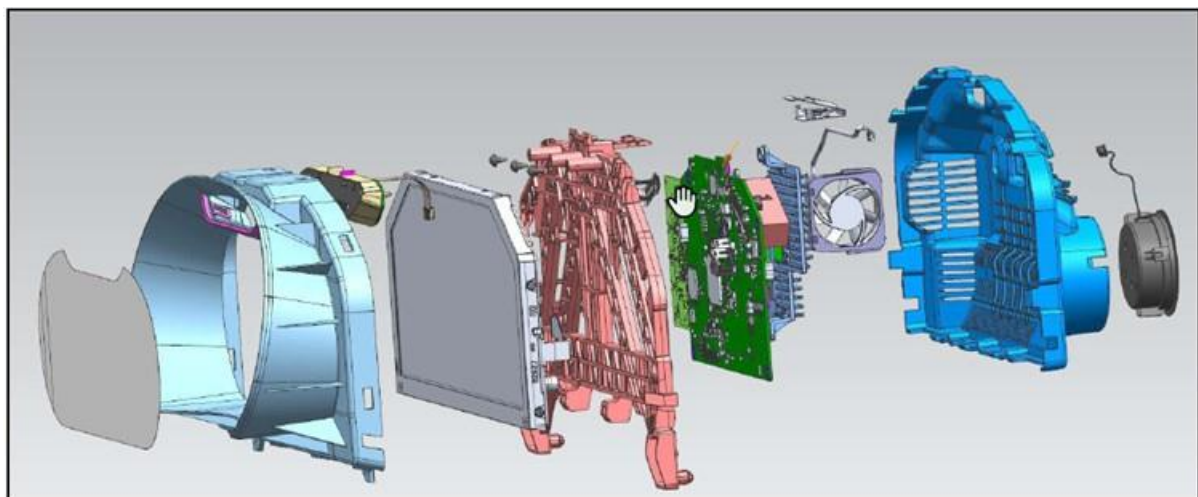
Exemplo 3D da montagem dos componentes de um produto final
